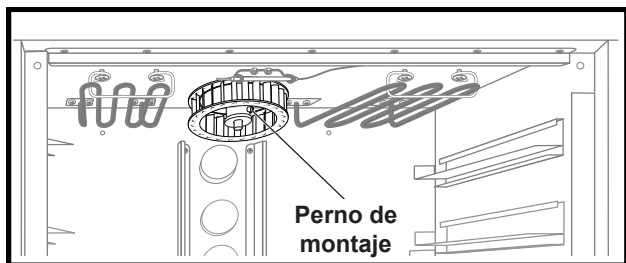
Perno de montaje de la rueda del ventilador del horno.
